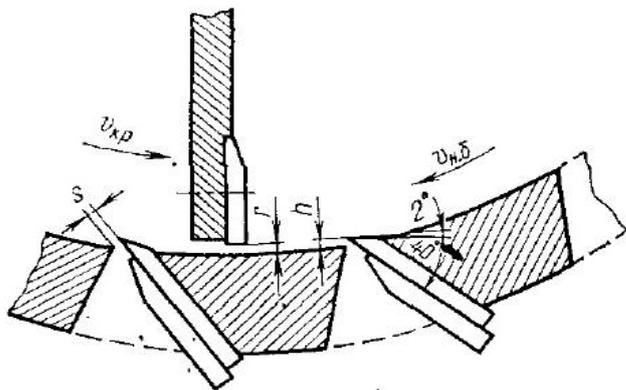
Схема узла резания центробежных стружечных станков [2]
